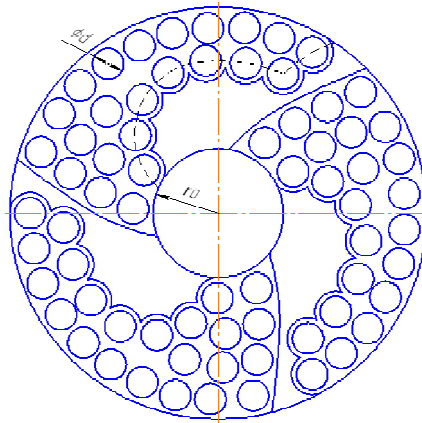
Конструкція інструмента для фінішної обробки ПСК
